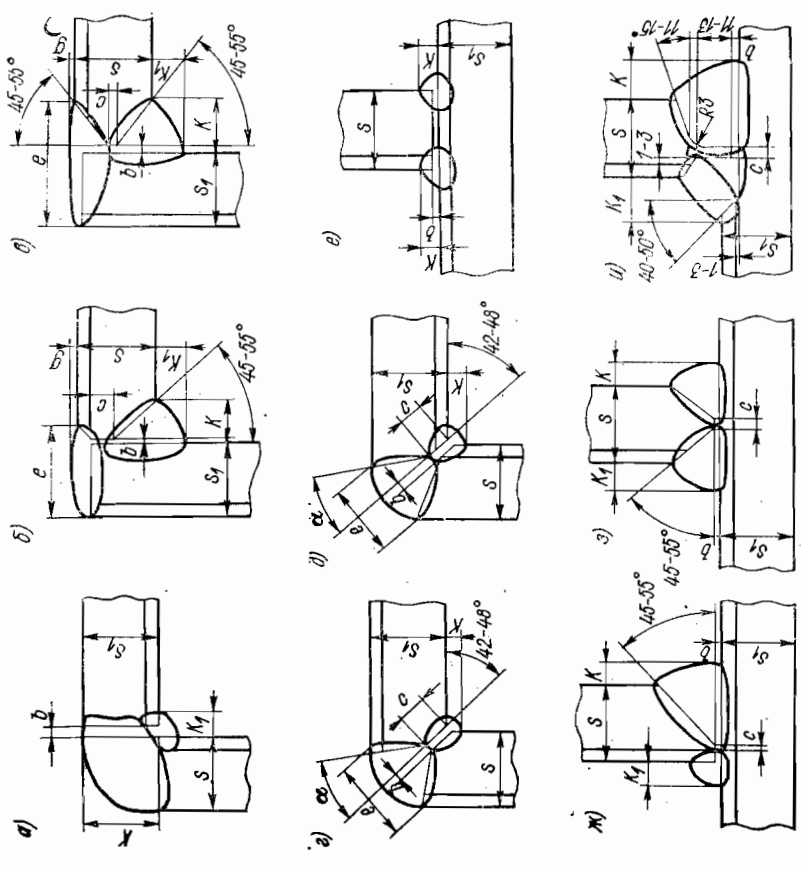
Конструкции двусторонних угловых (а-д) и тавровых (е-и) сварных соединений двуслойной стали: а, е — двусторонние без скоса кромок; б, ж — двусторонние со скосом одной кромки; в, з — с двумя скосами одной кромки; г, д, и — со скосом двух кромок
